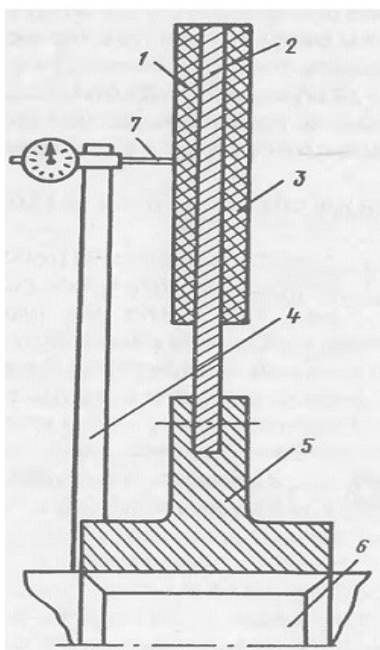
Контроль биения диска сцепления по боковым поверхностям:
